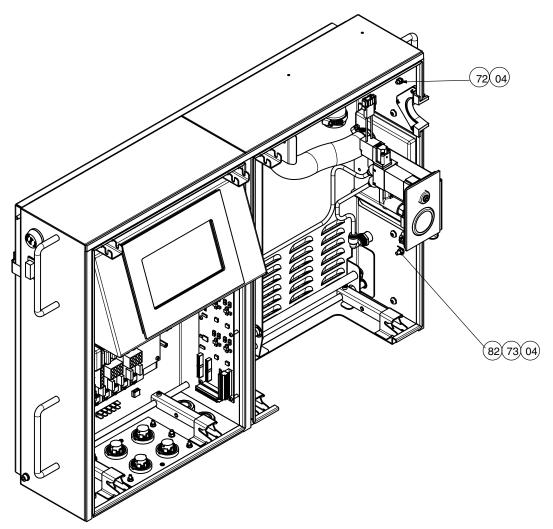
Baugruppe Chassis und Steuerung (3 von 3)
